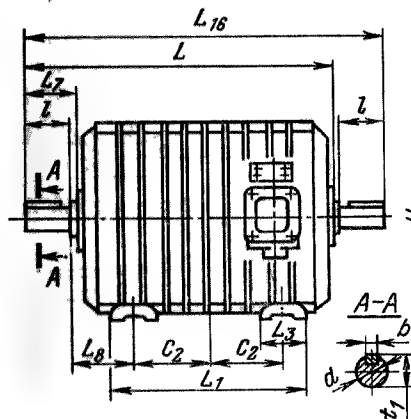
Габаритные и установочные размеры двигателей серии АР 4–8-го габаритов.
